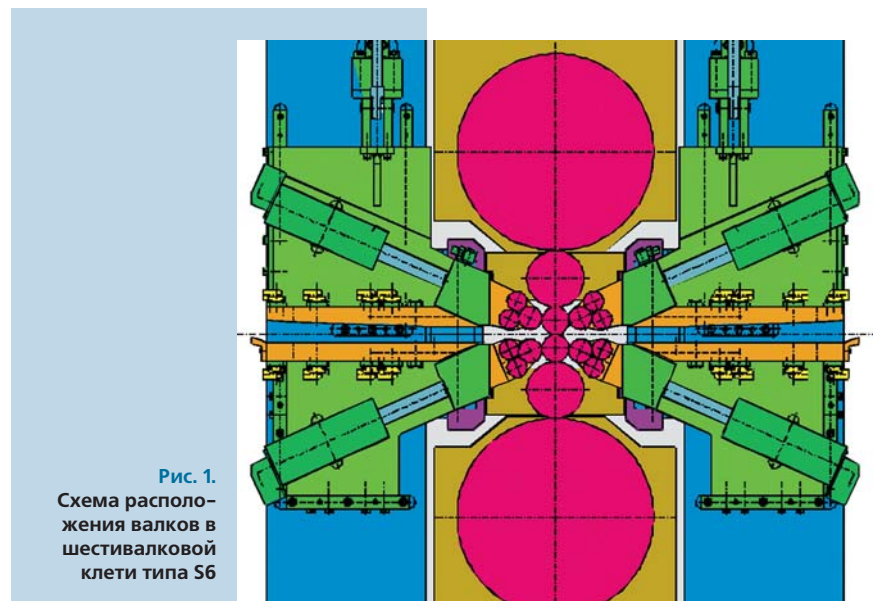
Схема расположения валков в шестивалковой клети типа S6
